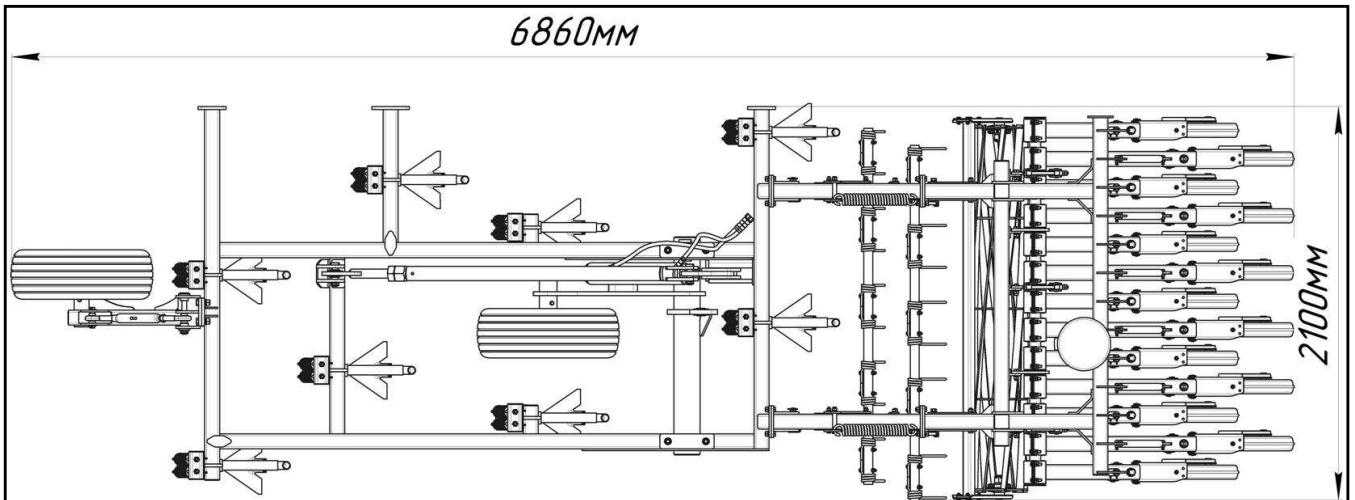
Вид погрузочного места № 2 крыла, при частичной разборке
